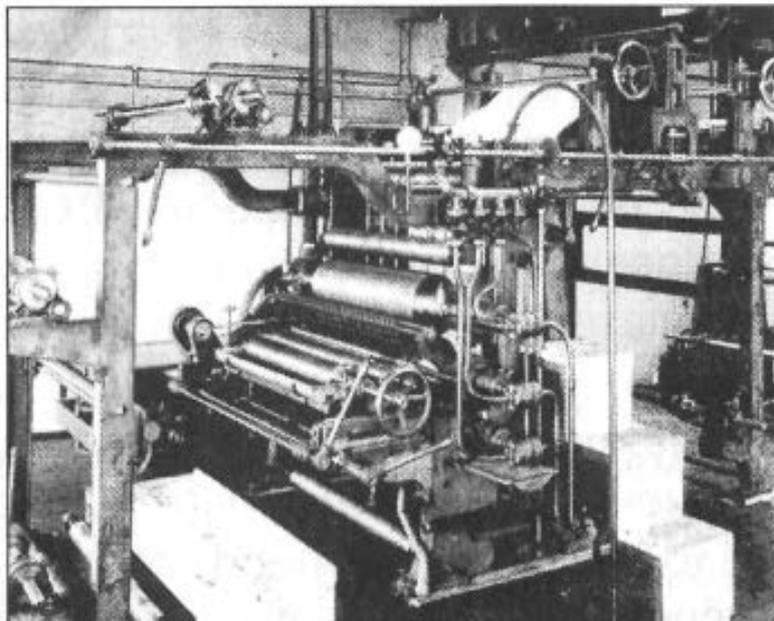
Машина для изготовления однослойного гофрокартона
